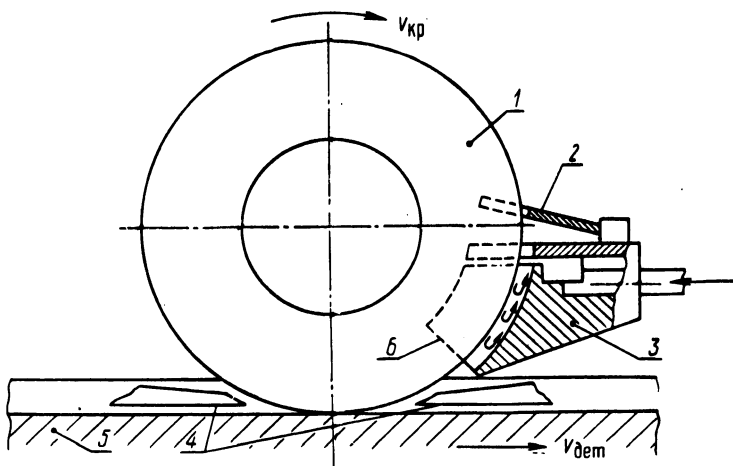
Схема устройства для подачи СОЖ при глубинном шлифовании пазов: 1 — шлифовальный круг; 2 — козырек для отражения воздушного потока; 3 — сопло для подачи СОЖ для очистки круга; 4 — сопла для подачи СОЖ в зону резания; 5 — обрабатываемое изделие; 6 — щиток.
